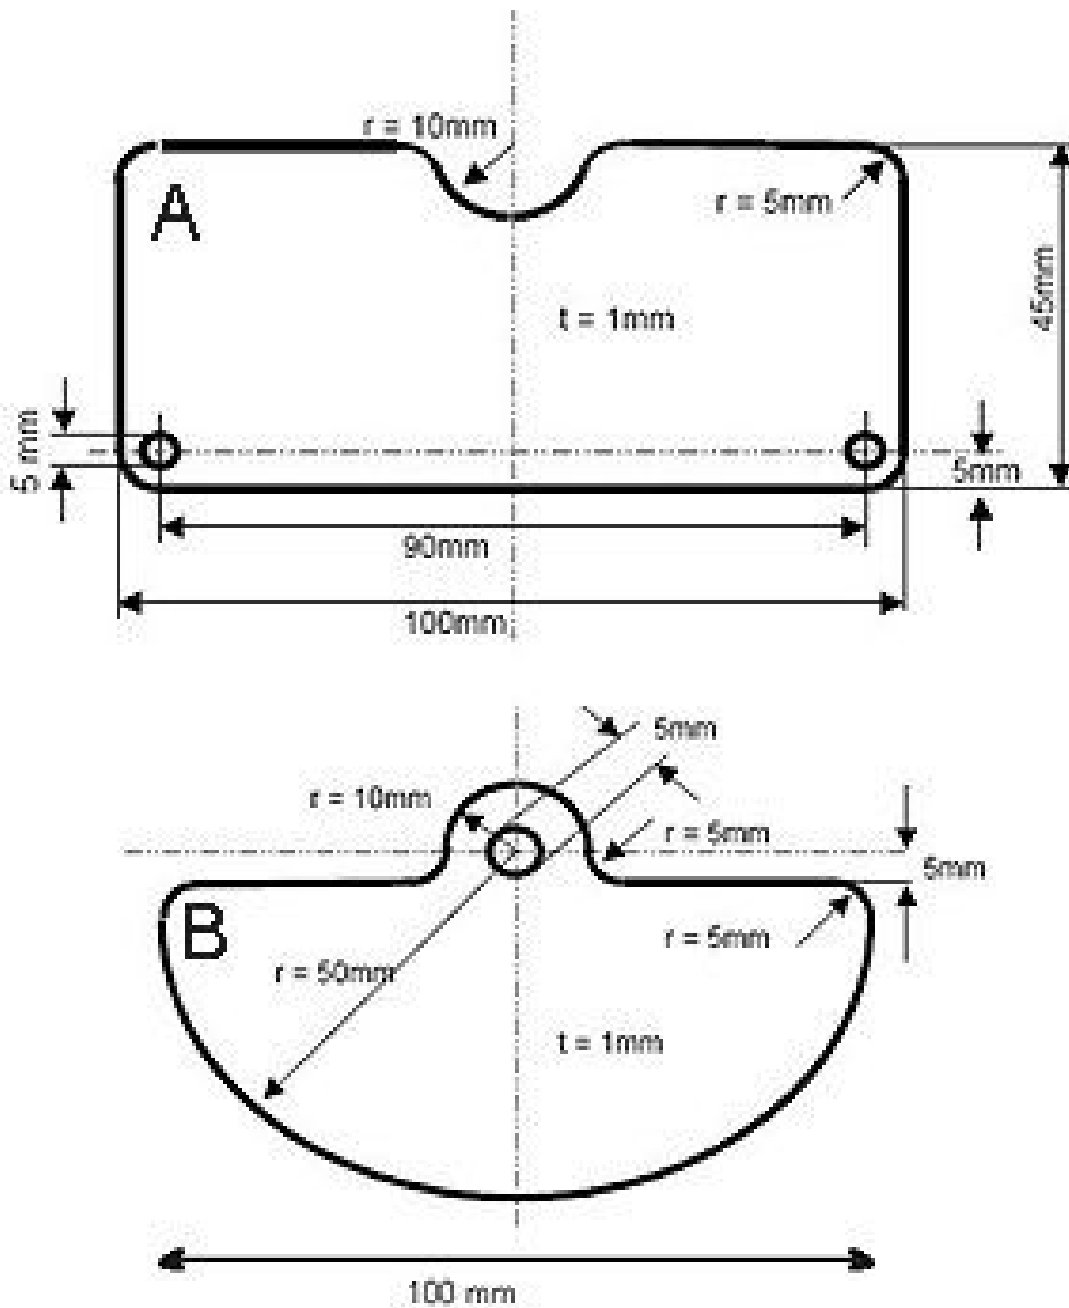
Dimensões das placas do estator (A) e do rotor (B).
